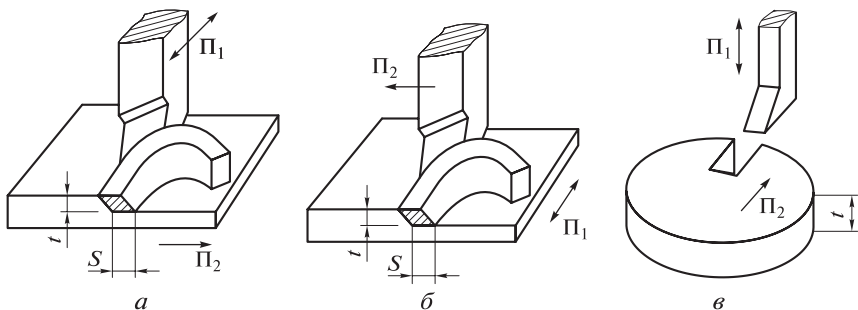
Формообразование обработанной поверхности и движения формообразования:
